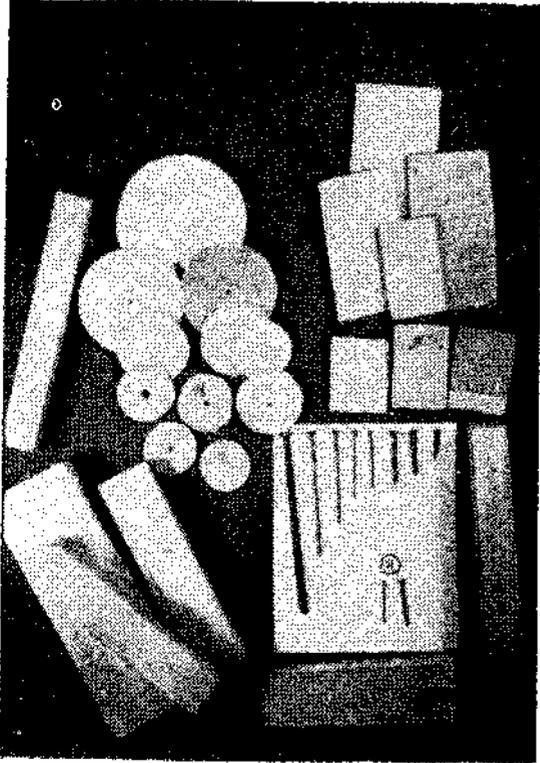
Таких форм и размеров были детали при отборе их для изготовления тележки
